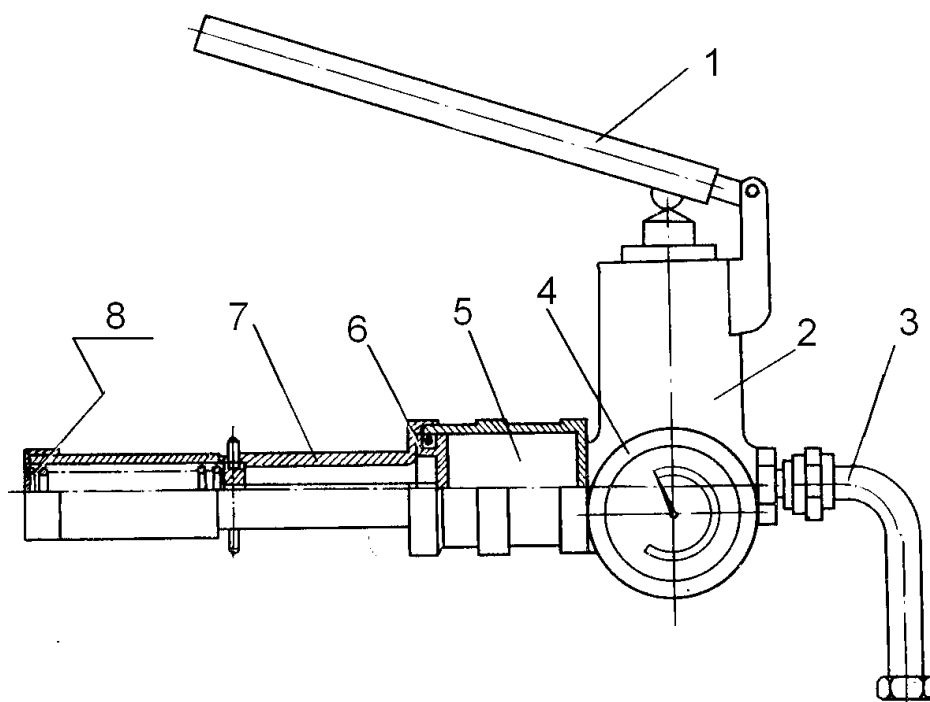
Приспособление КИ-9917 ГОСНИТИ для проверок форсунок:
